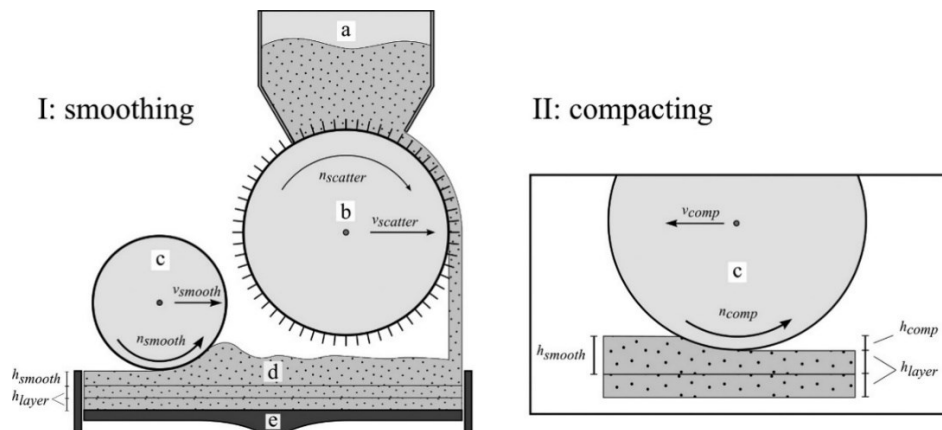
Základní druhy technologie Particle-bed 3D printing [25]
